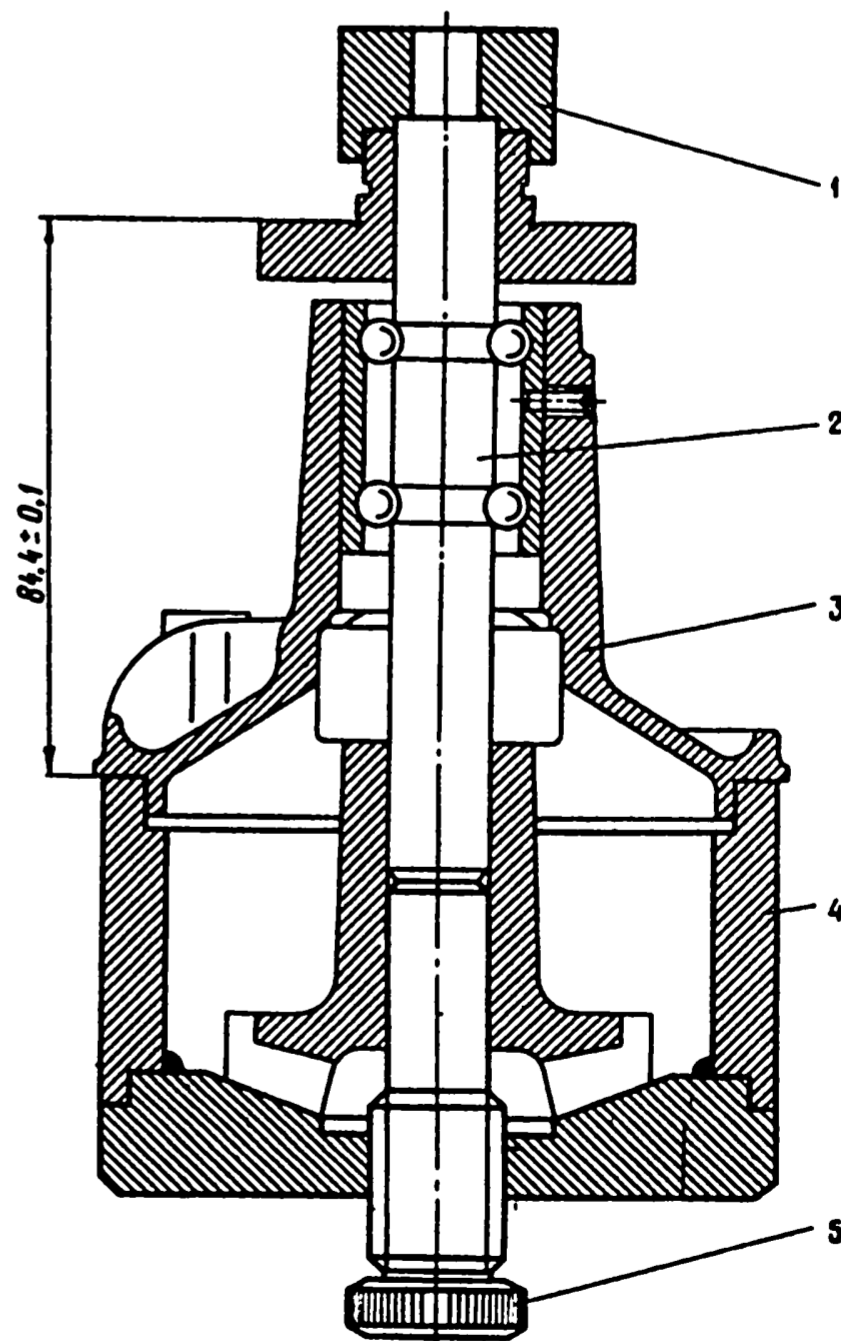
Напрессовка крыльчатки на валик насоса приспособлением А.60430: 1 - опора; 2 - валик насоса; 3 - крышка корпуса насоса; 4 - стакан; 5 - установочный винт
